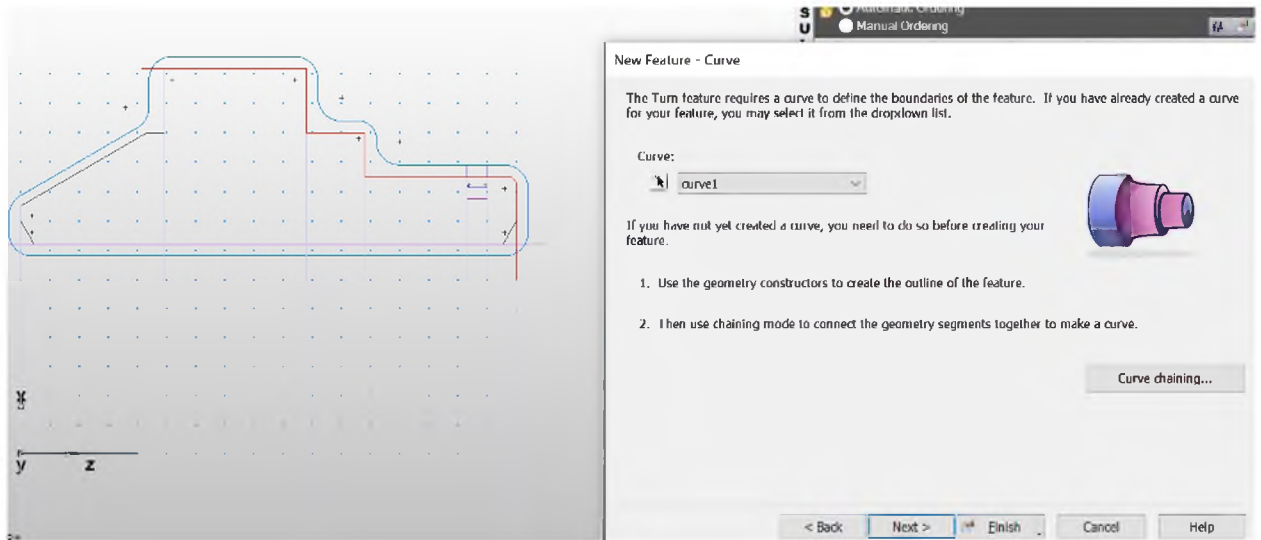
Траєкторія обробки зовнішньої поверхні
